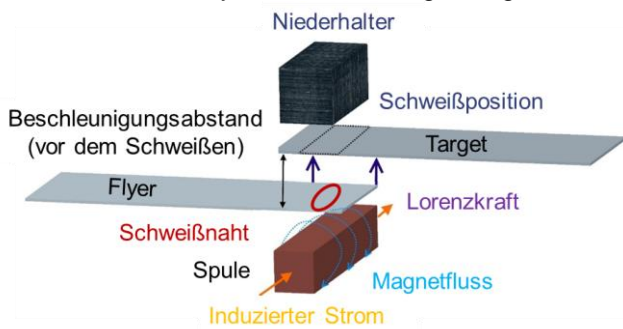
Prinzipskizze zum Magnetimpulsschweißen (MPS)
